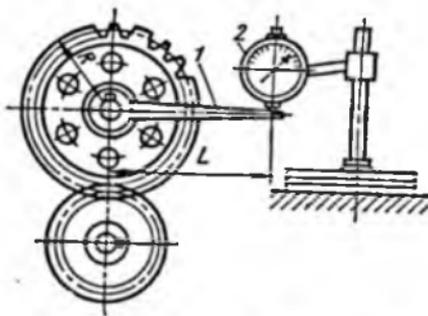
Прибор для проверки бокового зазора в зубчатом зацеплении
